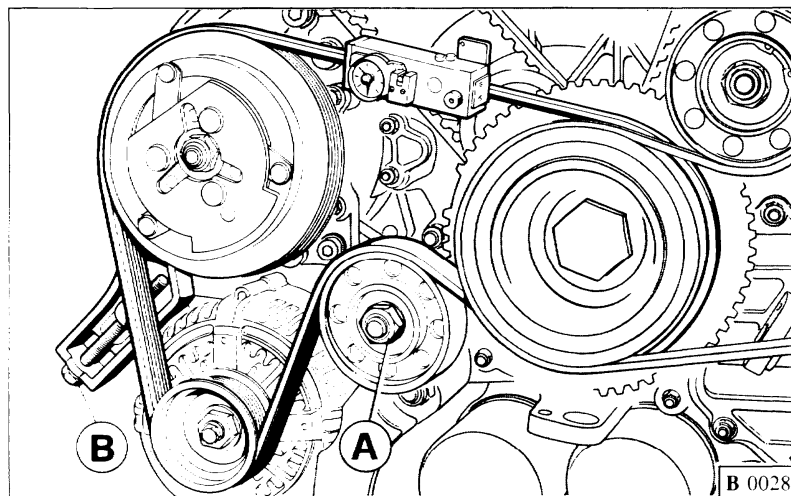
Tensione cinghia compressore A.C. e alternatore.
